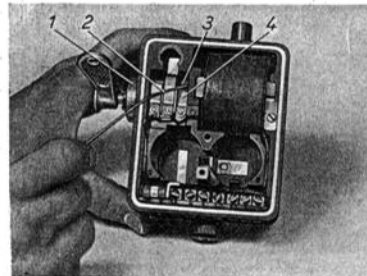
Zurückdrücken der hinteren Kontaktfeder mittels Draht beim Einführen der Schaltwalze
